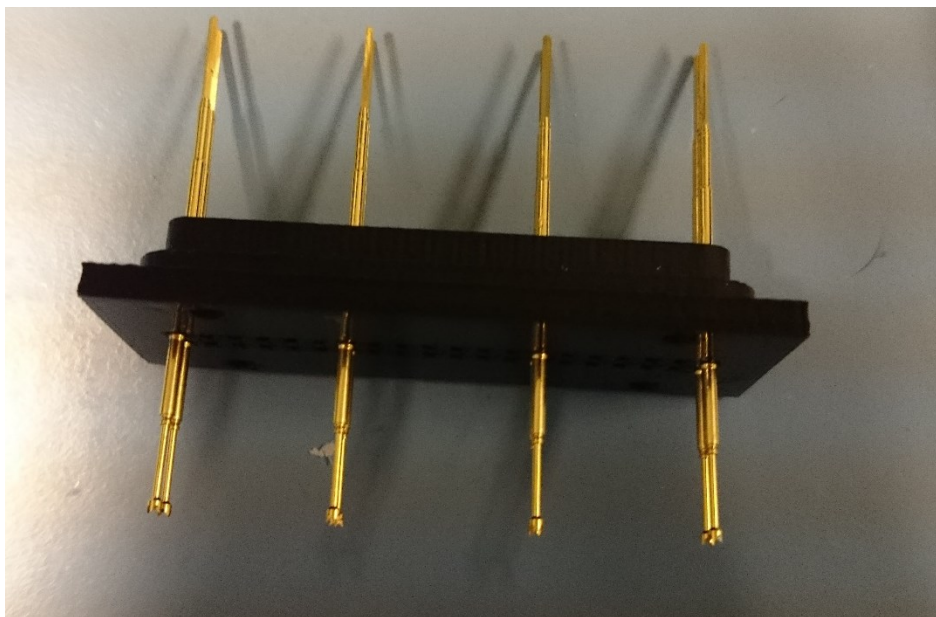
ABS-muovista tulostettu piirikortin pidike, jonka urissa viisteet.
